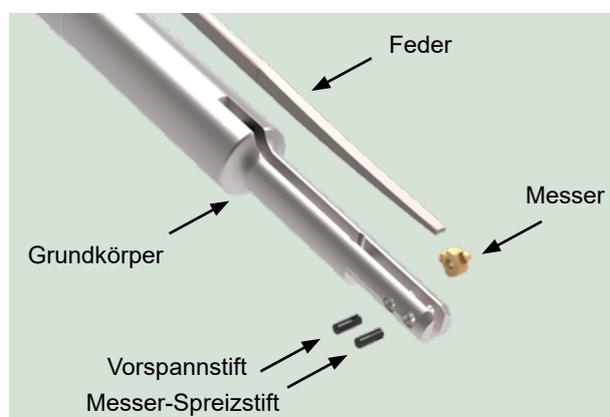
Für den Messerwechsel ist nur der vordere Spreizstift zu entfernen und die Feder auszuschwenken.
